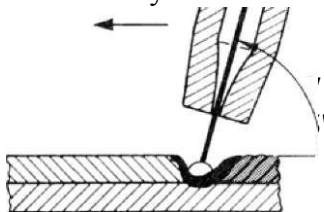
Положение горелки при сварке в среде защитного газа
